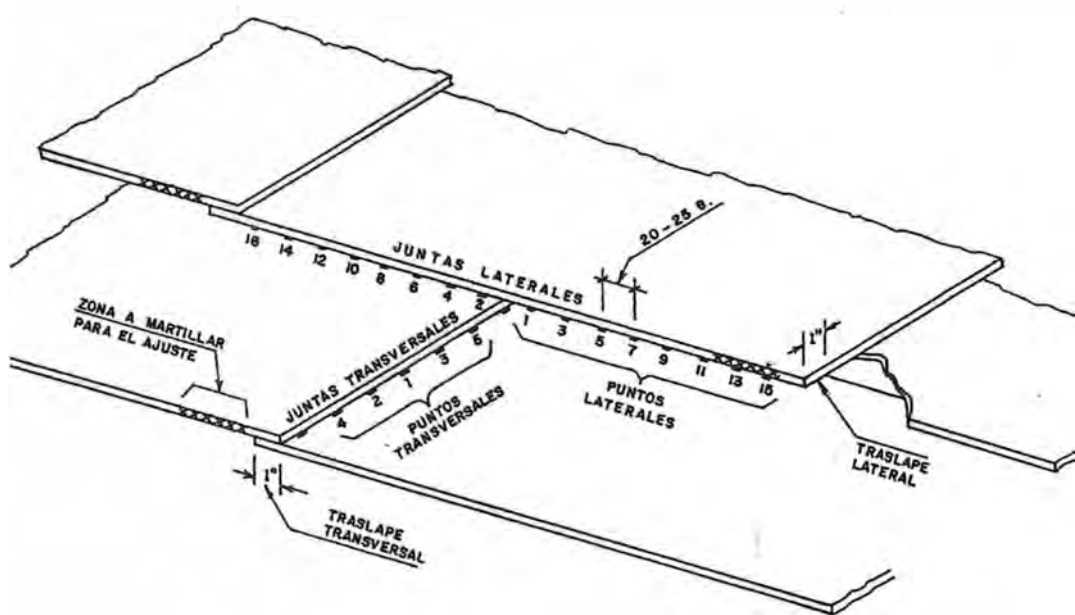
presentado y apuntalado de las planchas del fondo
